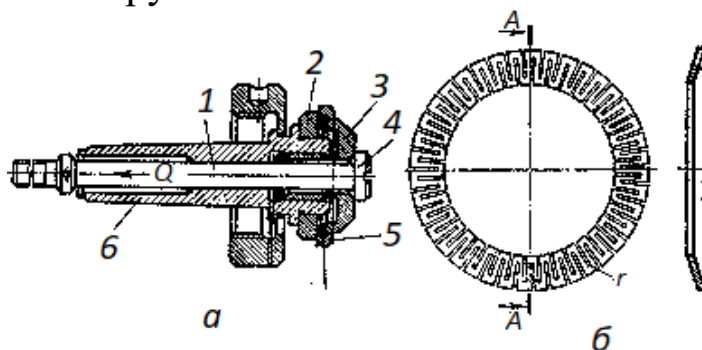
Консольная оправка с тарельчатыми пружинами (а) и тарельчатая пружина (б)
